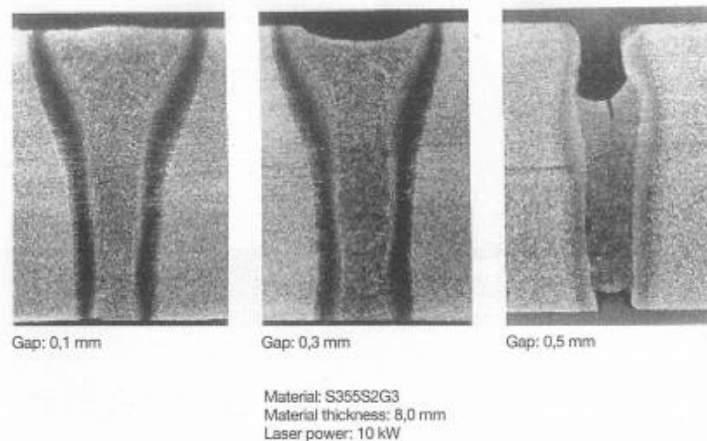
Macro secções de soldaduras com diferentes largura de folga, [2].
